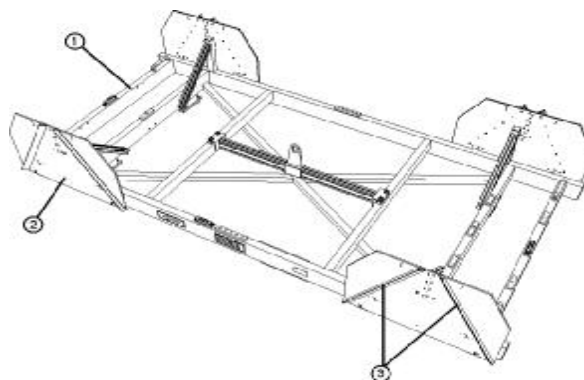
Эскиз приспособления калибровочного Master Gauge
